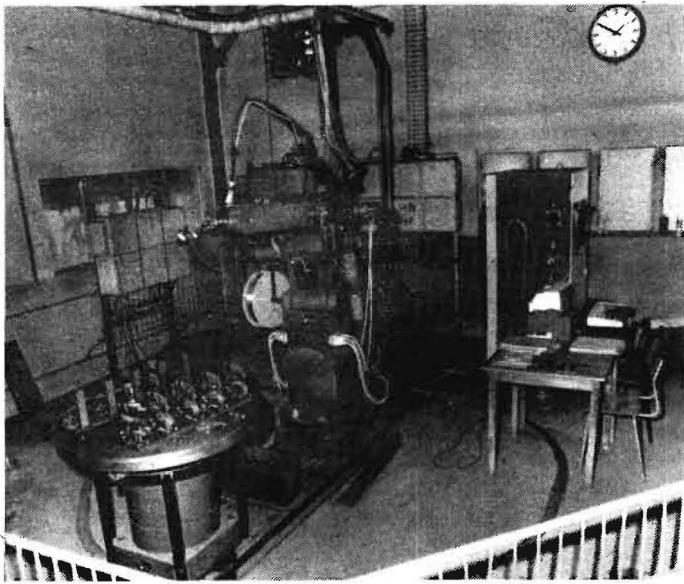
Lichtbogenschweißeinheit TEL 750 mit Schweißvorrichtung „Stützbügel“
